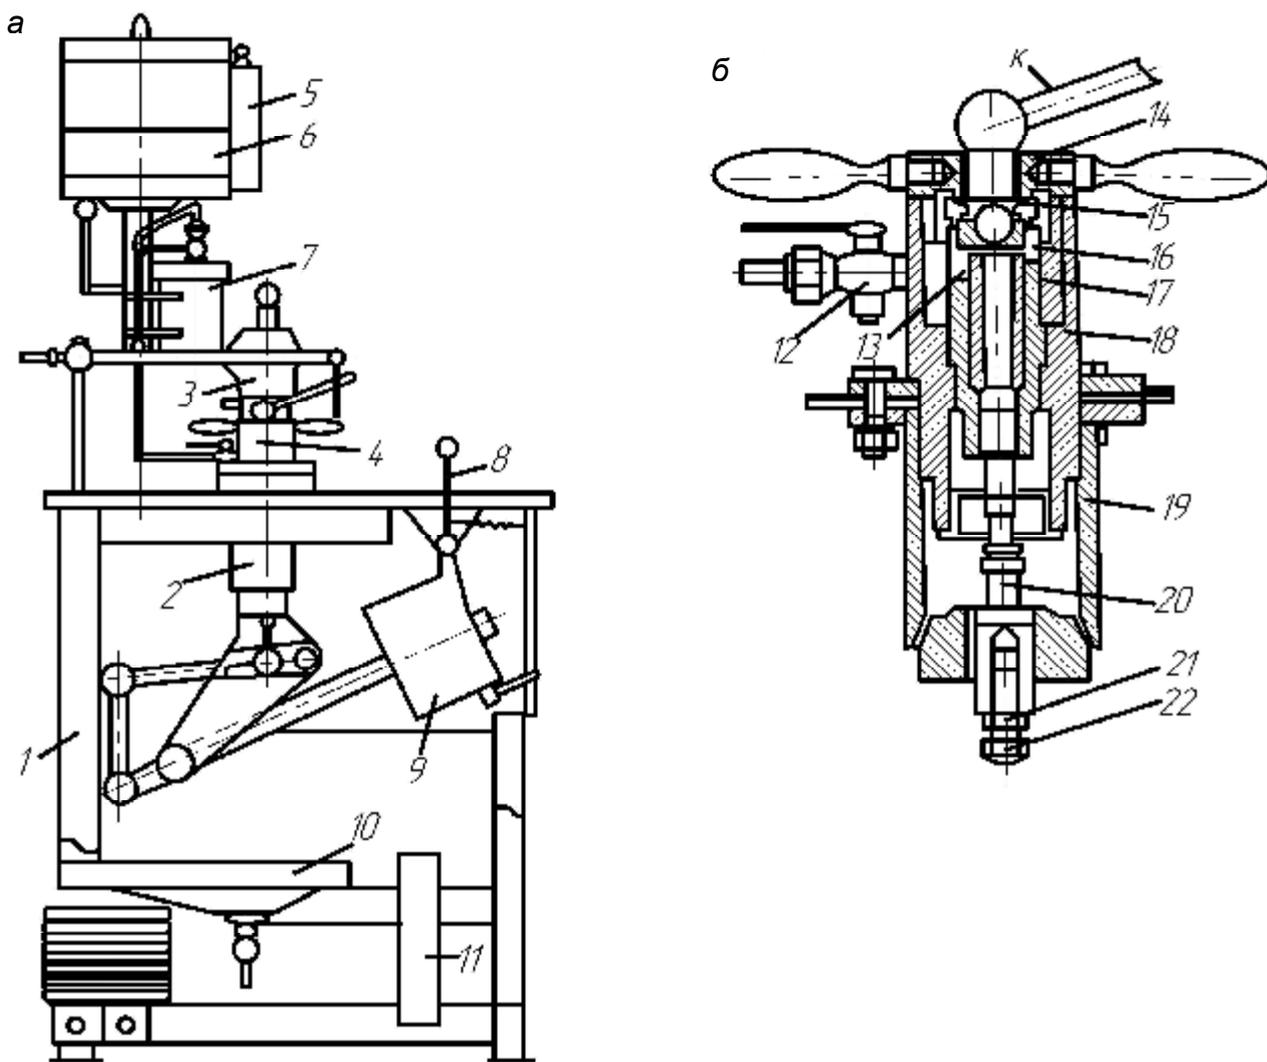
Стенд А53 для проверки плунжерных пар: а – эскиз стенда: 1 – стол; 2 – устройство для проверки плотности плунжерной пары; 3 – контролируемый топливный насос; 4 – фиксатор; 5 – указатель уровня топлива; 6 – топливный бак; 7 – фильтр; 8 – ручная защелка; 9 – груз; 10 – поддон; 11 – буферное устройство; б – эскиз установки плунжерной пары: 12 – кран; 13 – фиксирующий винт; 14 – крышка; 15 – прижимной винт; 16 – уплотнитель; 17 – установочная втулка; 18, 19 – верхний и нижний корпуса; 20 – толкатель; 21 – контргайка; 22 – регулировочный болт
